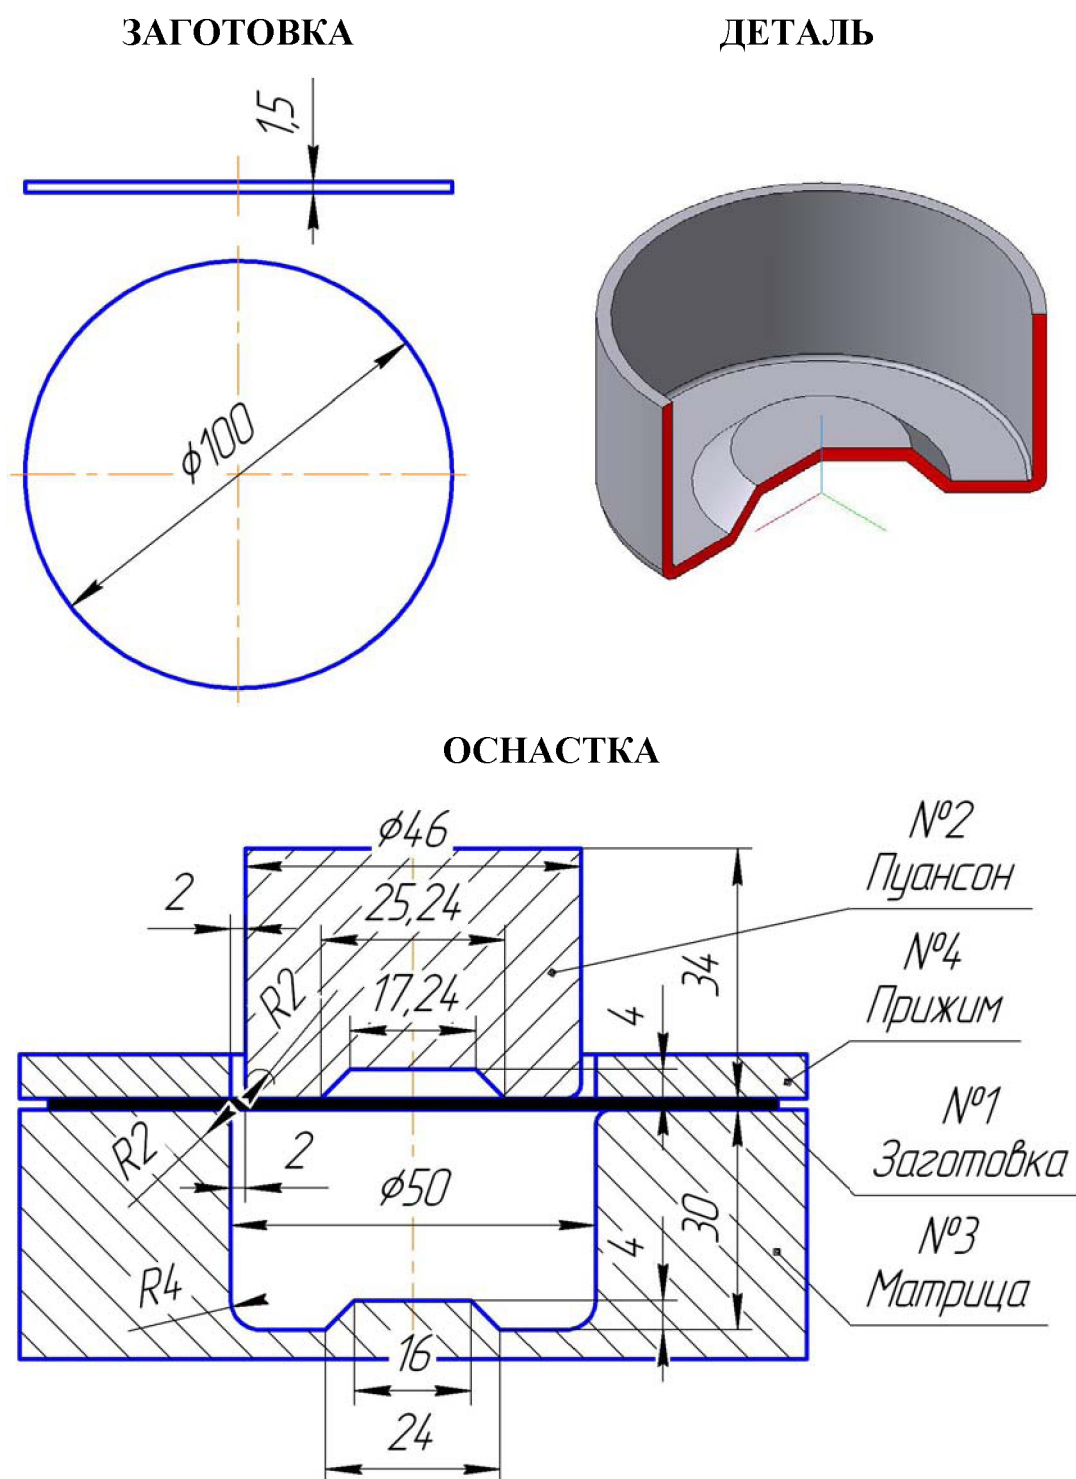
Оснастка и заготовка для процесса вытяжки
